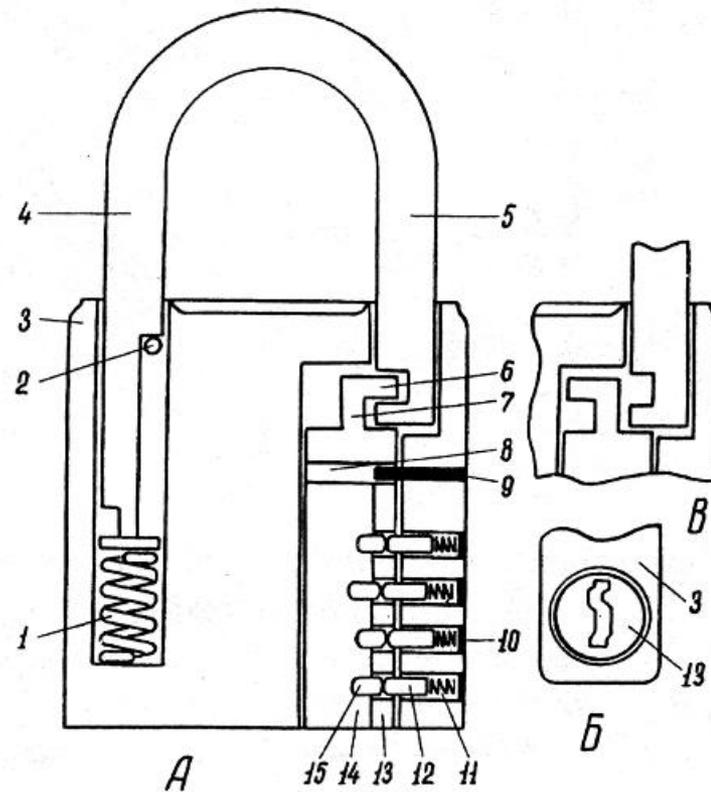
Устройство висячего цилиндрического замка с литым корпусом:
